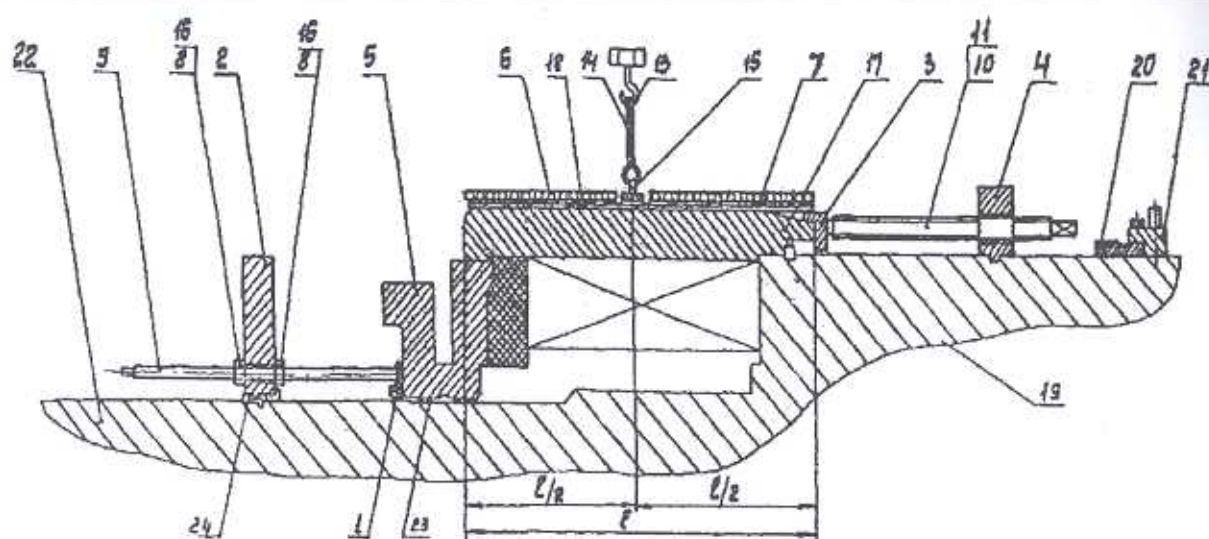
Установка приспособлений и снятие бандажного кольца с ротора:
